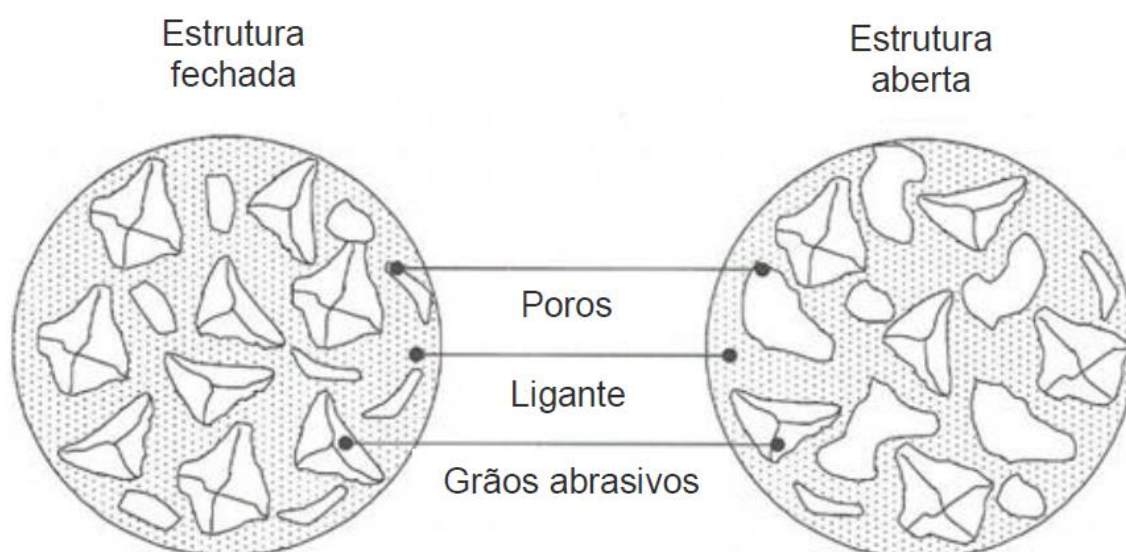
Estrutura de um rebolo de retificação (PORTO, 2004 - adaptado).
